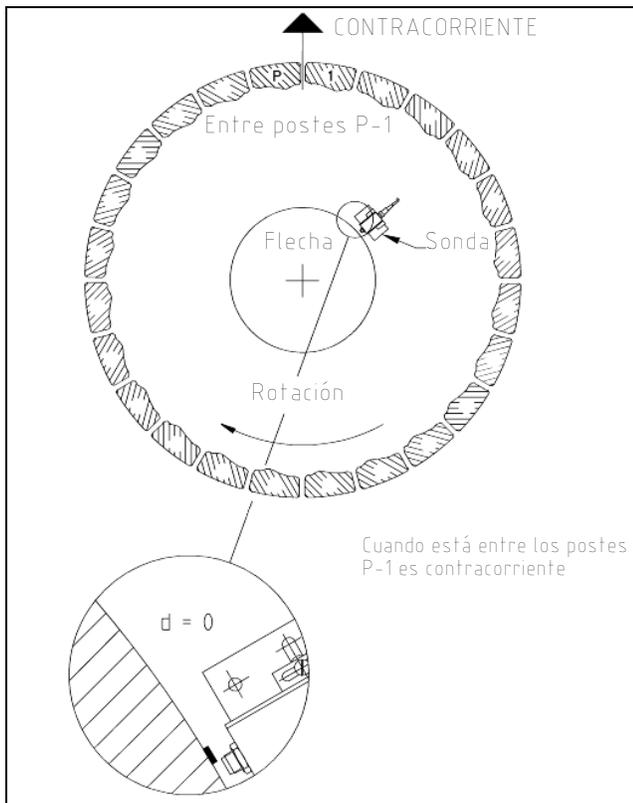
La posición P-1 sobre el rotor apunta a contracorriente
